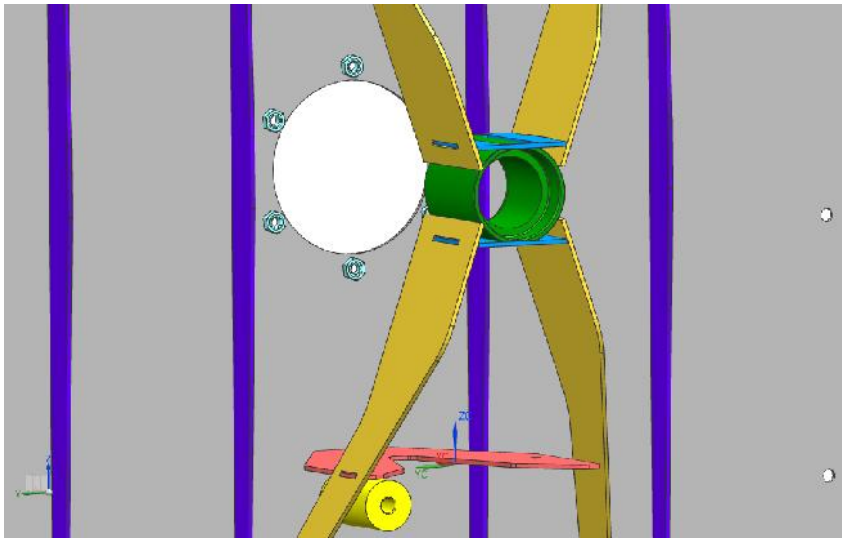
Detailansicht Schweißrahmen
